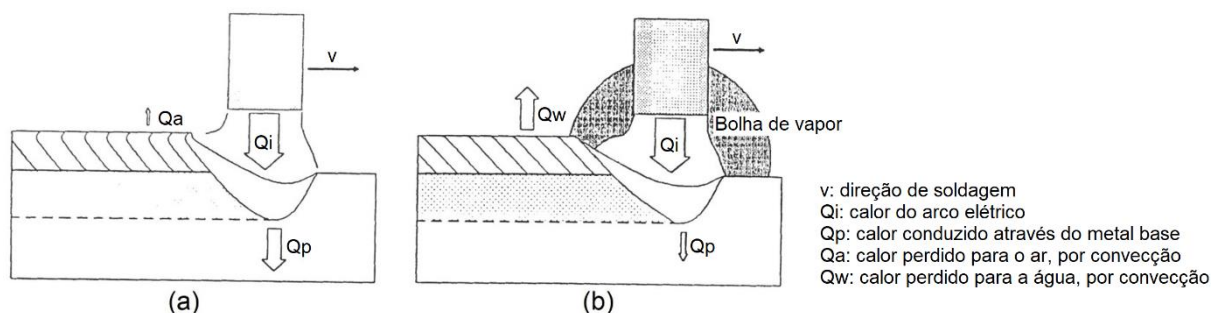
Desenho esquemático indicando as trocas de calor: (a) soldagem ao ar e (b) soldagem subaquática.
